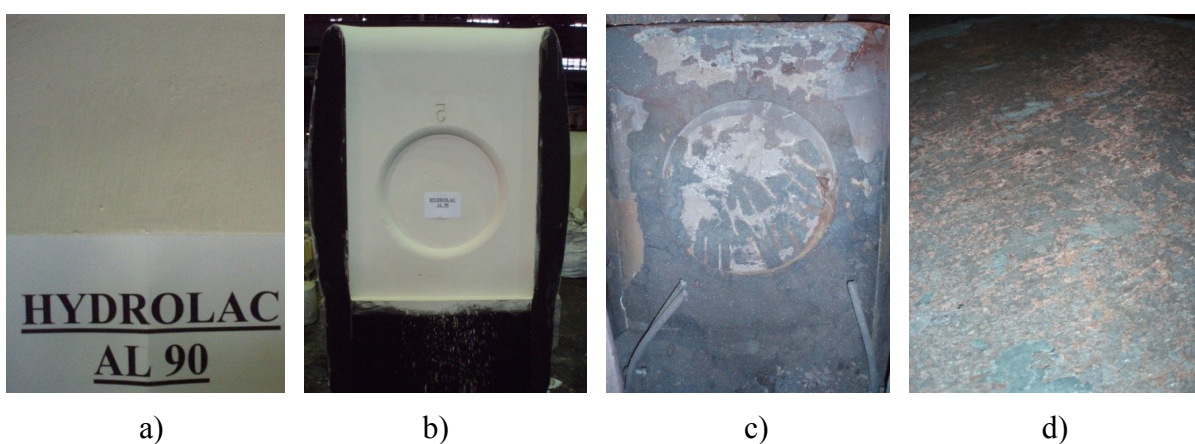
Jádru číslo 3 – a) detail naneseného nátěru, b) detail jádra, c) plocha náboje po odlití, d) detail povrchu odlitku před tryskáním
